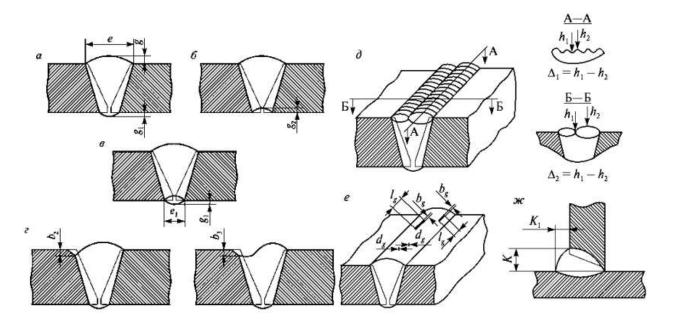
Конструктивные элементы и дефекты сварного шва, подлежащие измерительному контролю
